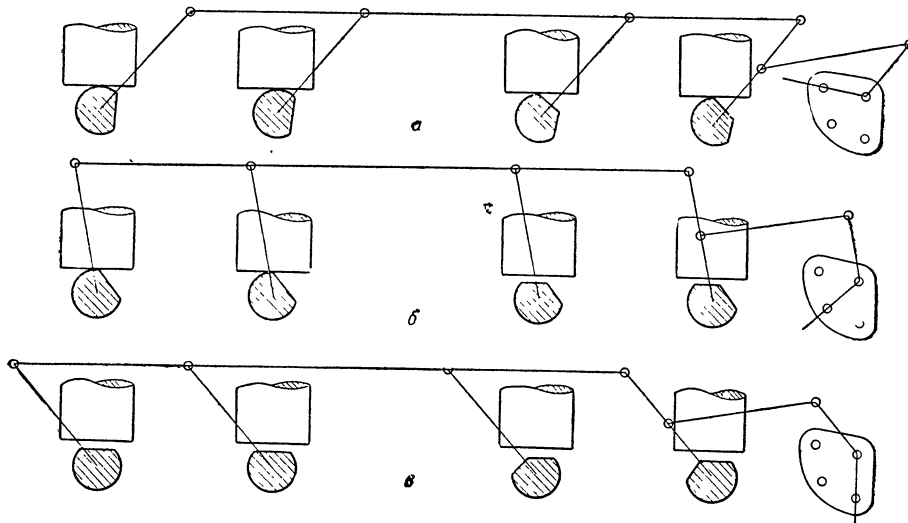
Схема установки механизма декомпрессии дизелей Д-54А и Д-75 в положения:
